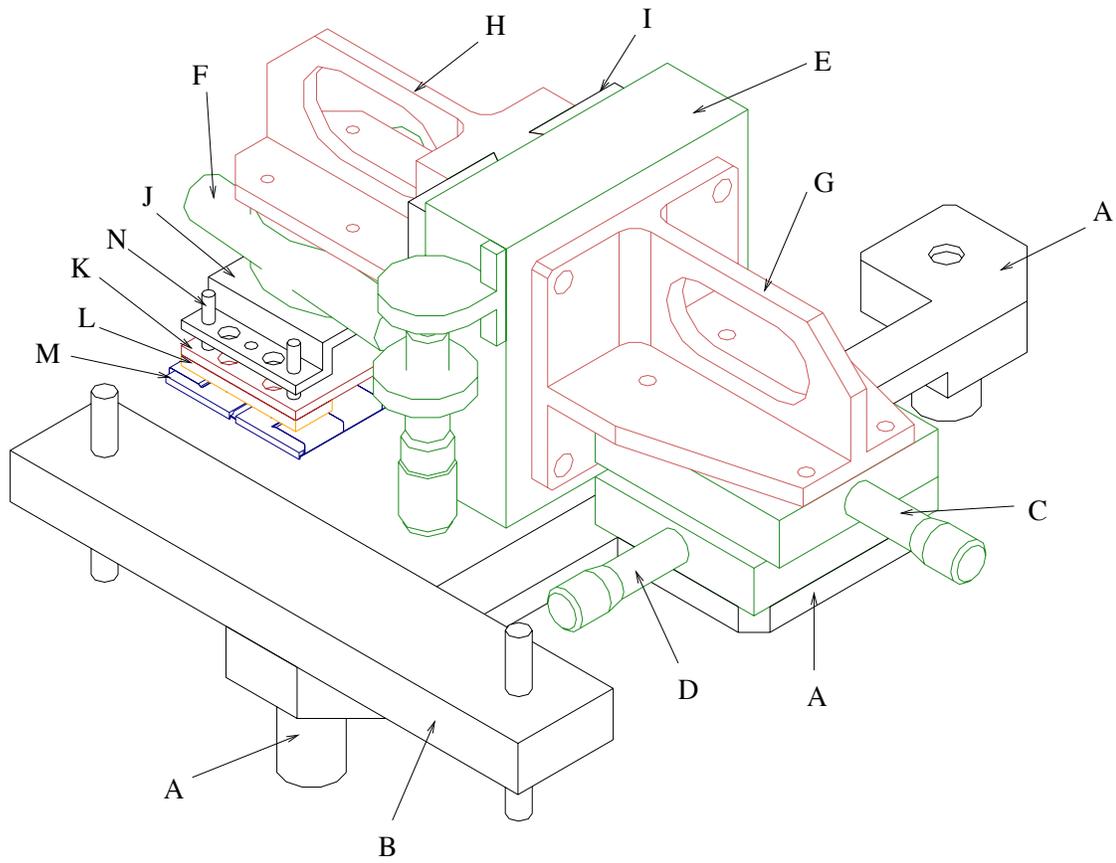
Vue en trois dimensions de l'outil de préhension.
